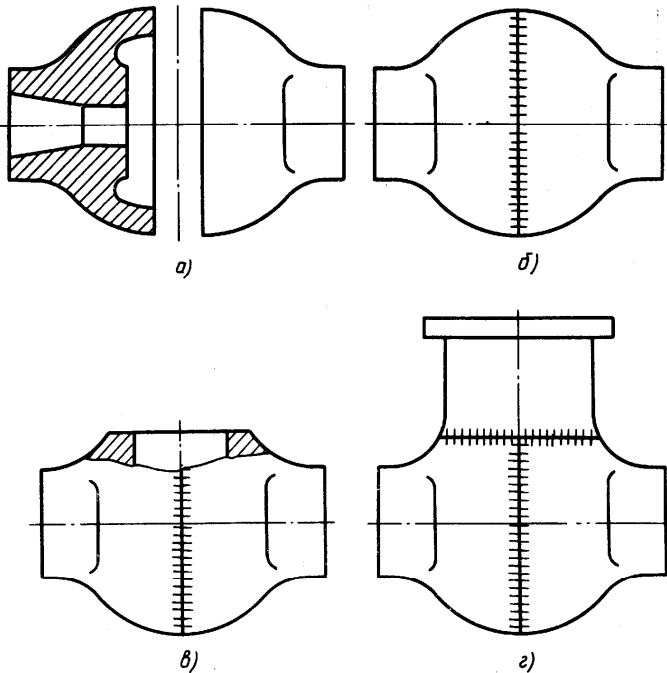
Последовательность изготовления корпуса арматуры в штампосварном исполнении
